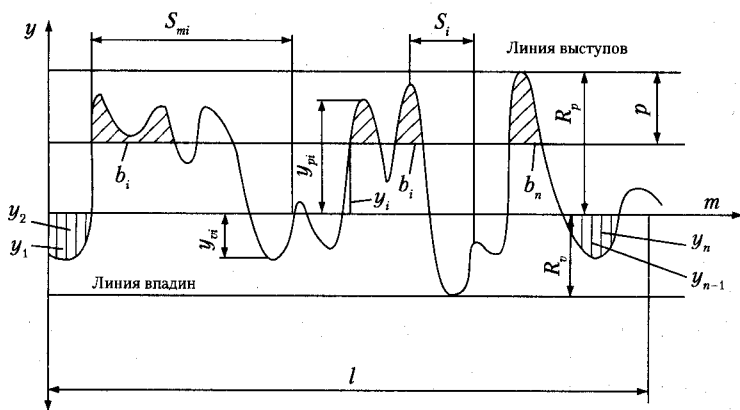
Профилограмма и основные параметры шероховатости поверхности
